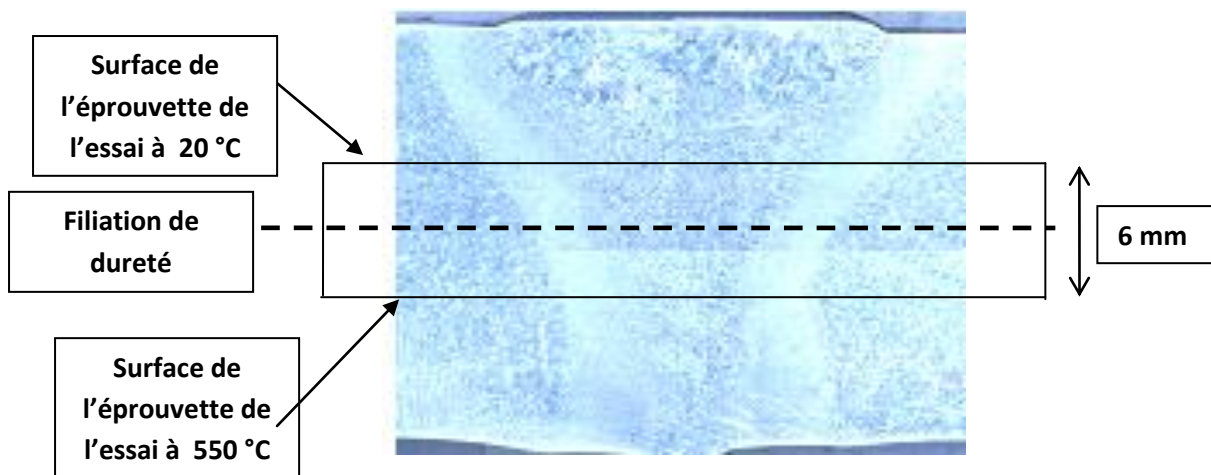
prélèvement de l'éprouvette dans le joint soudé.
